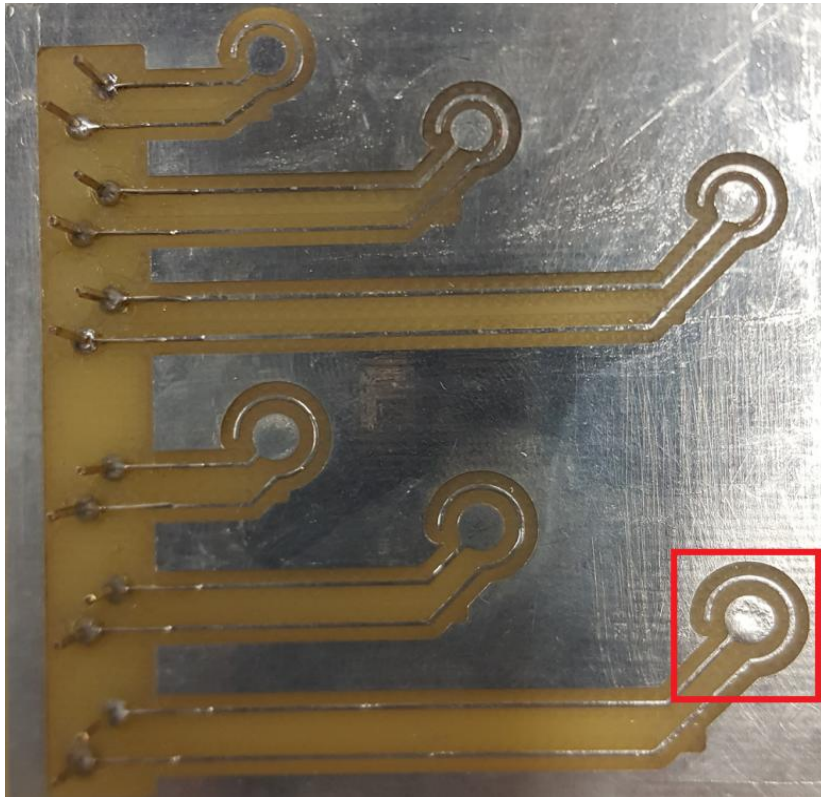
PCB con técnica de CNC. En rojo el electrodo seleccionado.
